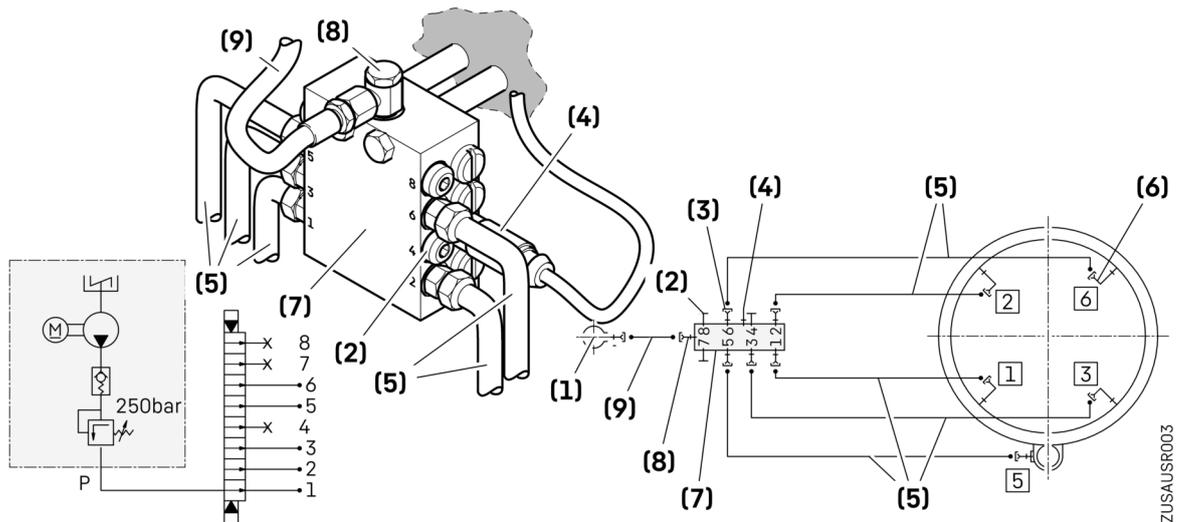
Verlegeplan und Hydraulik-Schaltplan (8er-Verteiler mit einem Drehwerk)
